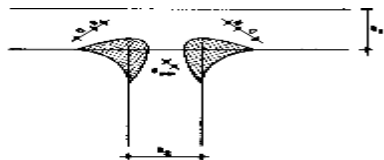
A Penetración de una soldadura en ángulo
